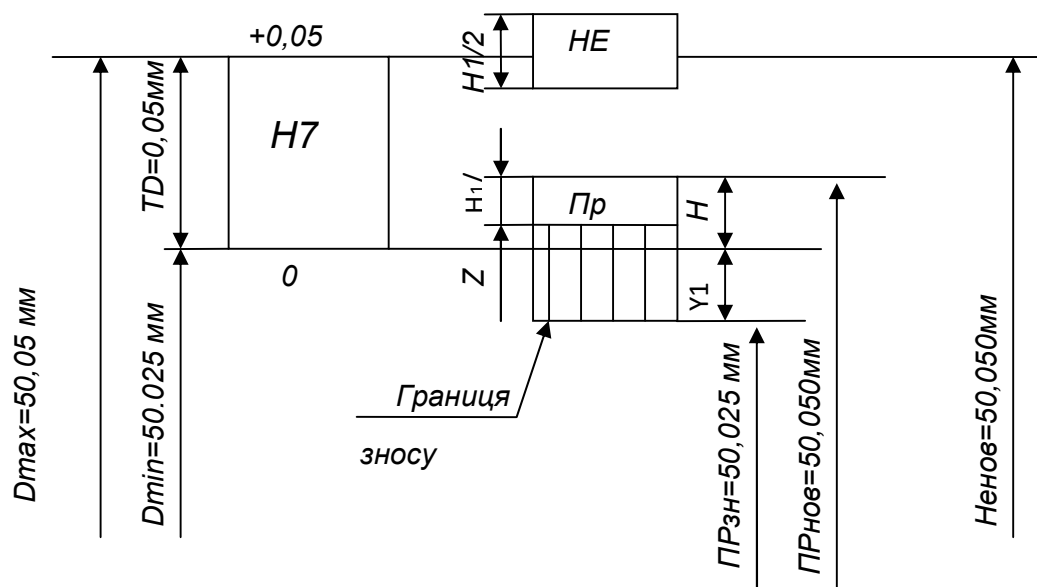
Схема розташування полів допусків калібру–пробки
